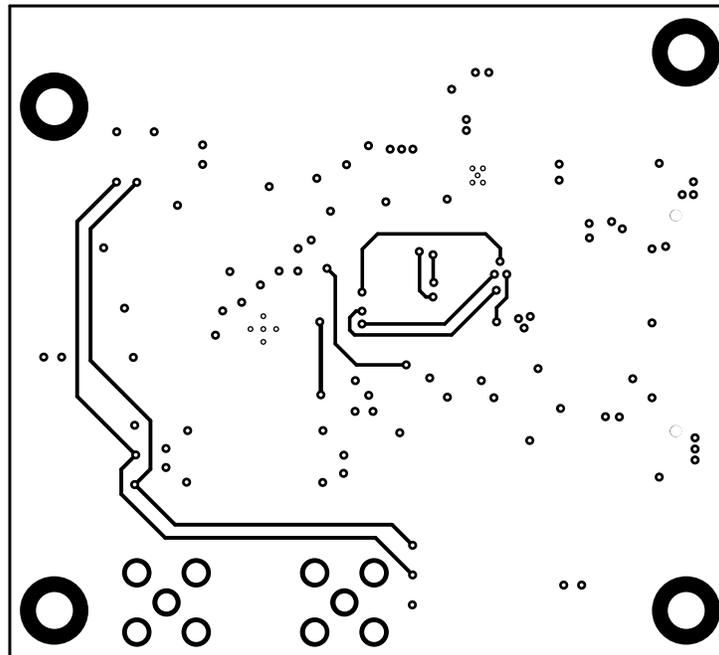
ADS8681WEVM PCB 第 4 层 - 底层
